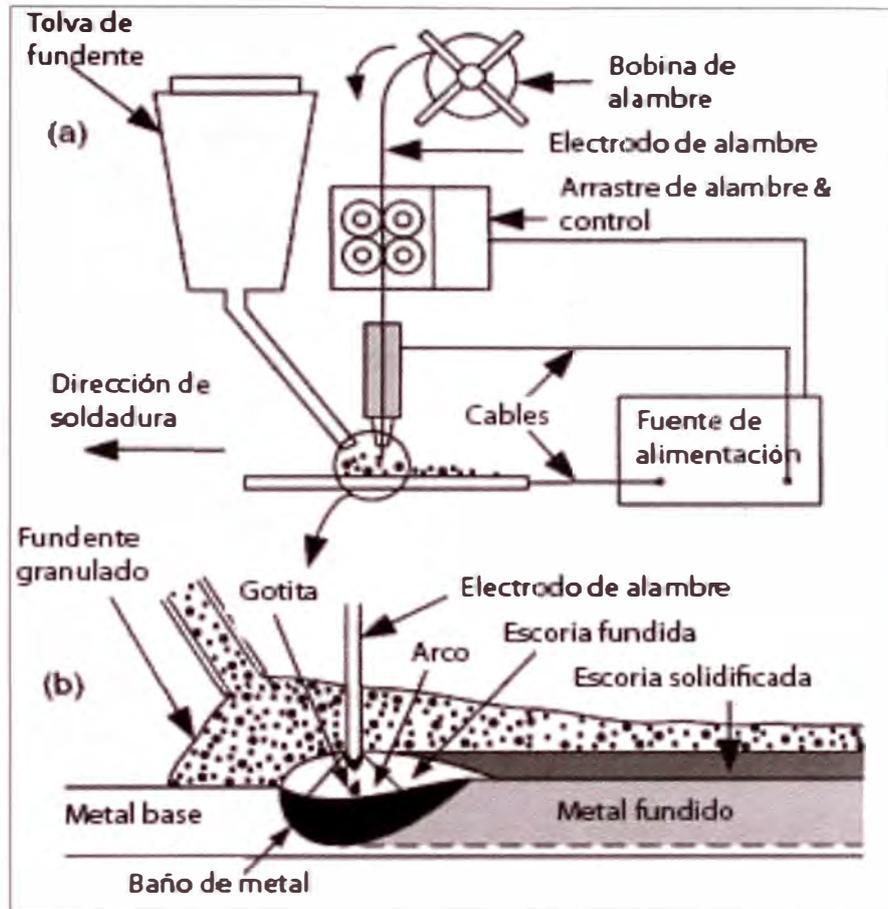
Esquema del proceso de soldadura SAW
